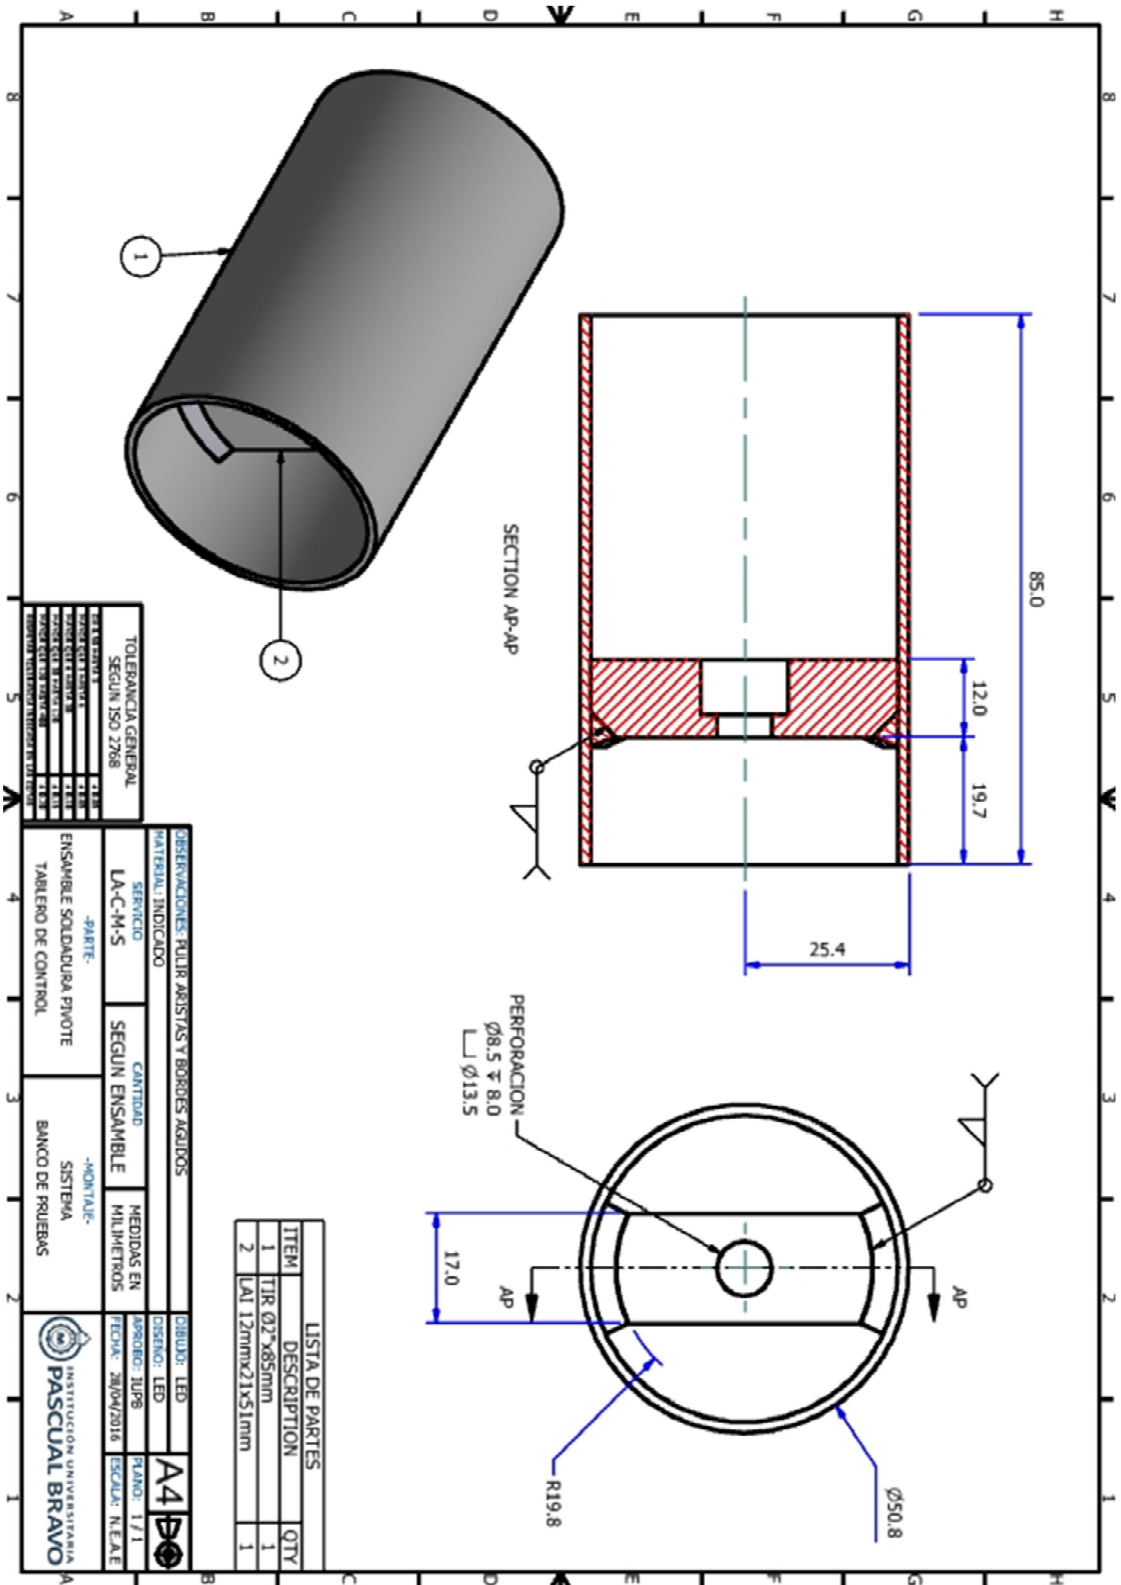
Ensamble soldadura pivote tablero de control
